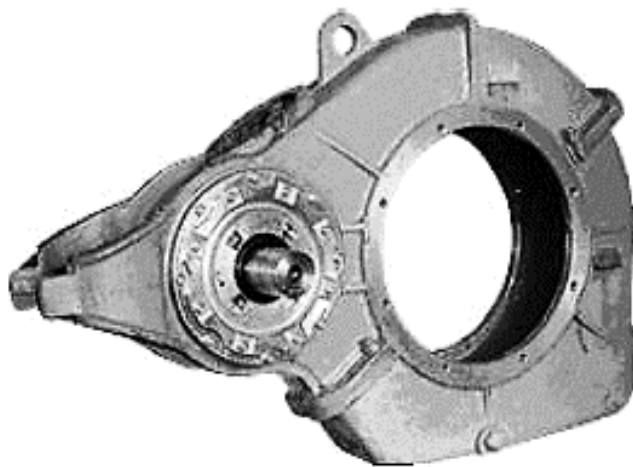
Загальний вигляд корпусу тягового редуктора з модульним вузлом малої шестірні
